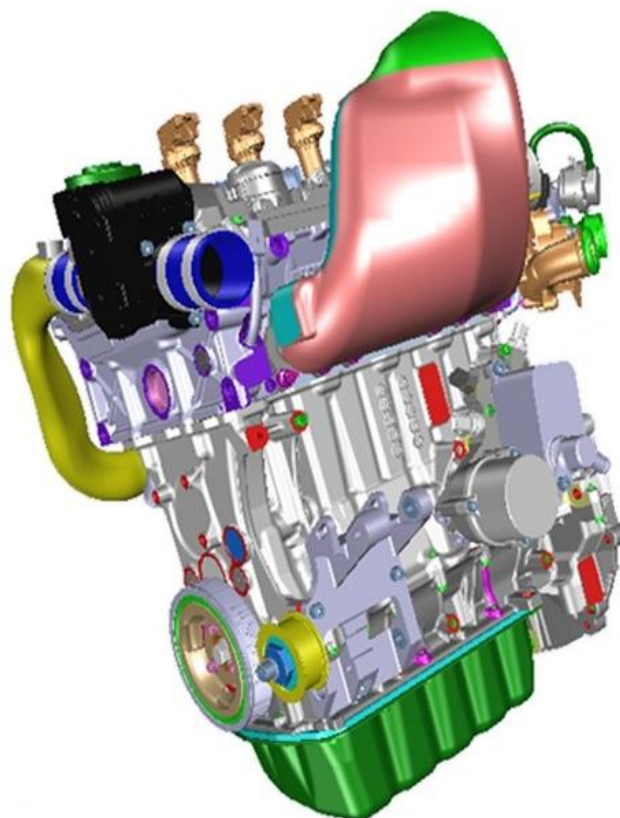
Representación esquemática del conjunto motor turboalimentado montado
